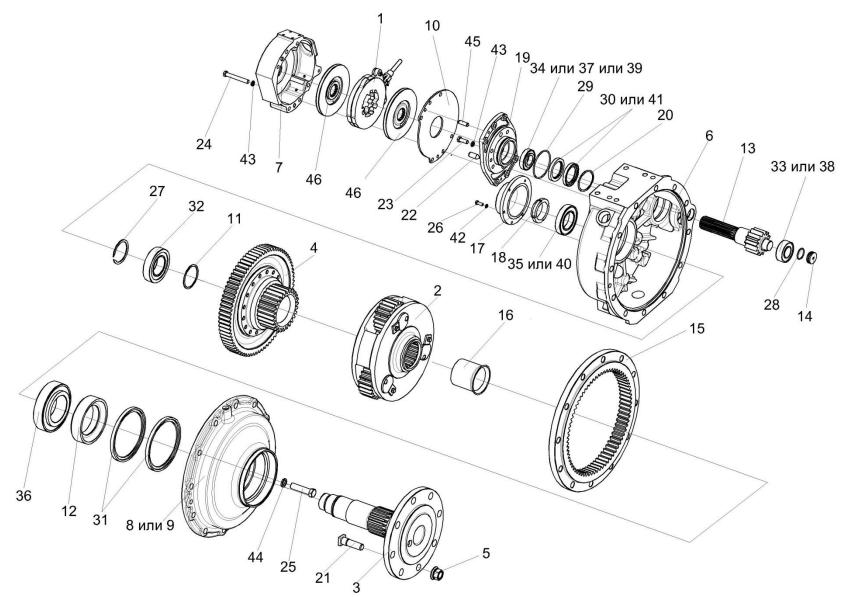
Редуктор бортовой правый УЭС 0107070А-04 (лист 2)
